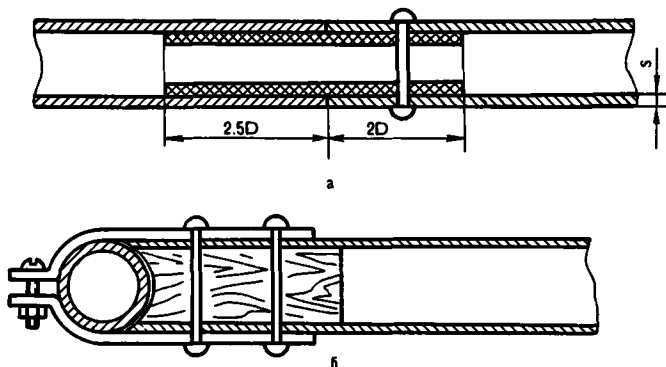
Способы соединения продольных и поперечных элементов каркаса из труб
